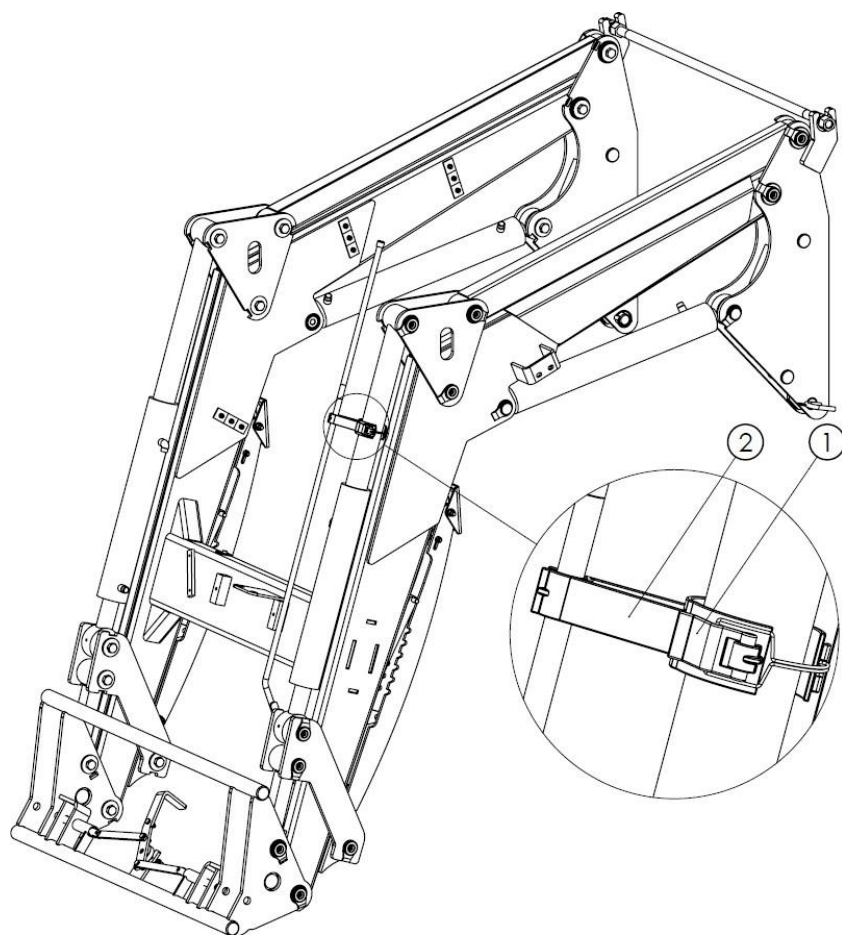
Регулировка указателя (защелка - поз. 1, опору - поз. 2)
